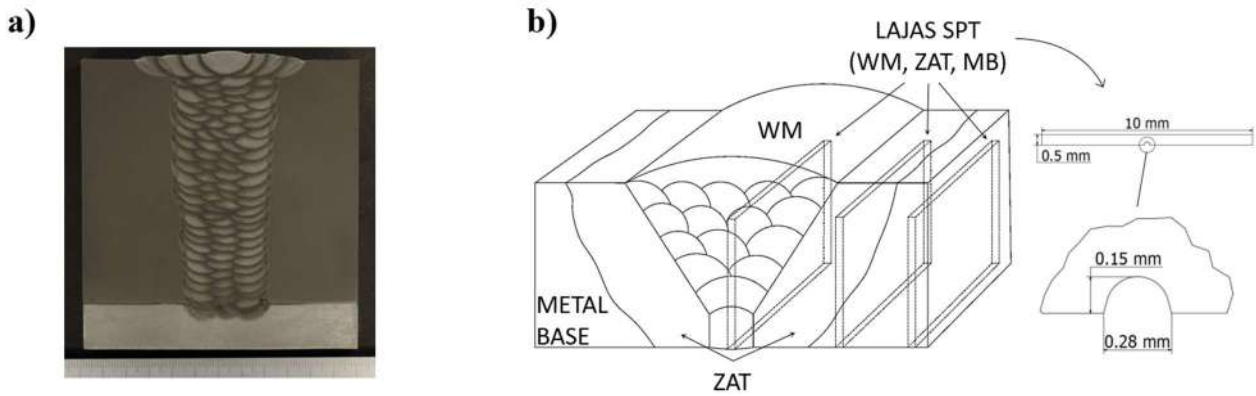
Aspecto general de la unión soldada: a) macrografía, b) esquema de extracción de las probetas SPT
